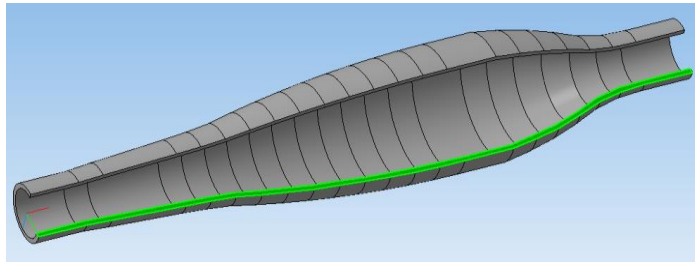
Ескіз розрахованого контуру робочої поверхні резонаторної труби
